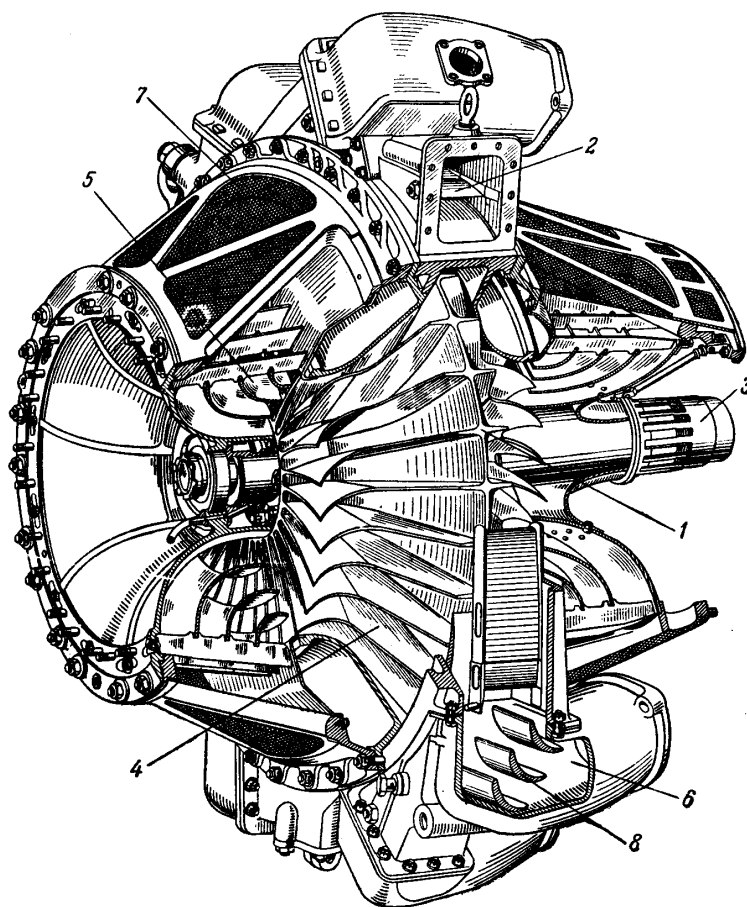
Jednoproudový letecký turbokompresorový motor s odstředivým kompresorem s oboustranným oběžným kolem VK-1
